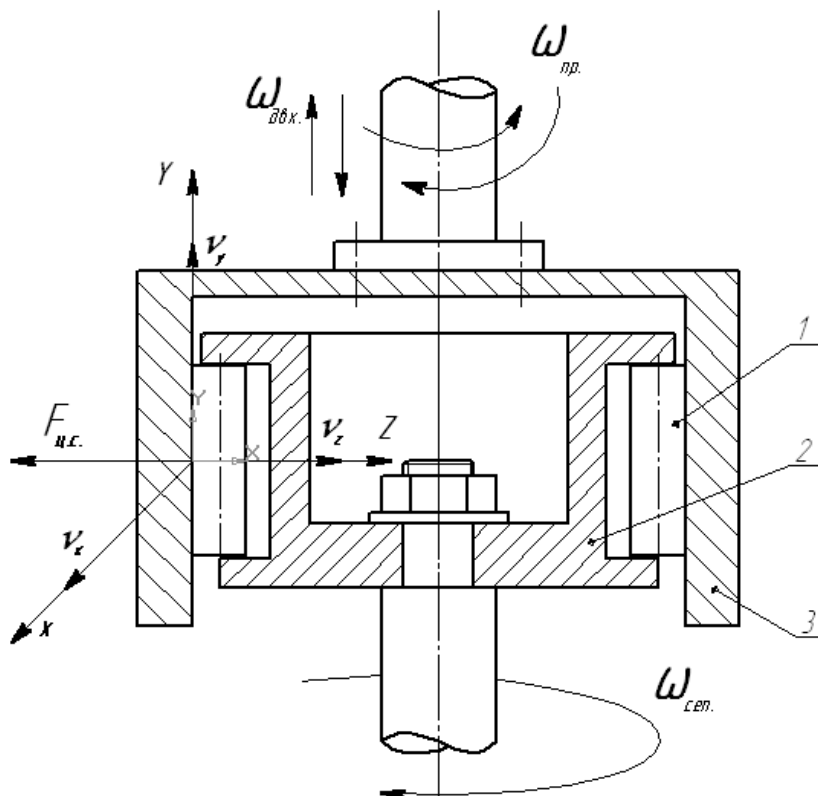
Кинематическая схема процесса абразивной доводки наружных цилиндрических поверхностей.
